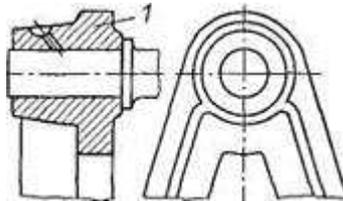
Неразъемный подшипник скольжения: 1 — станина
